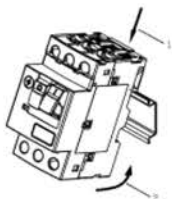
Установка автоматического выключателя ВА-431 на дин-рейку.
